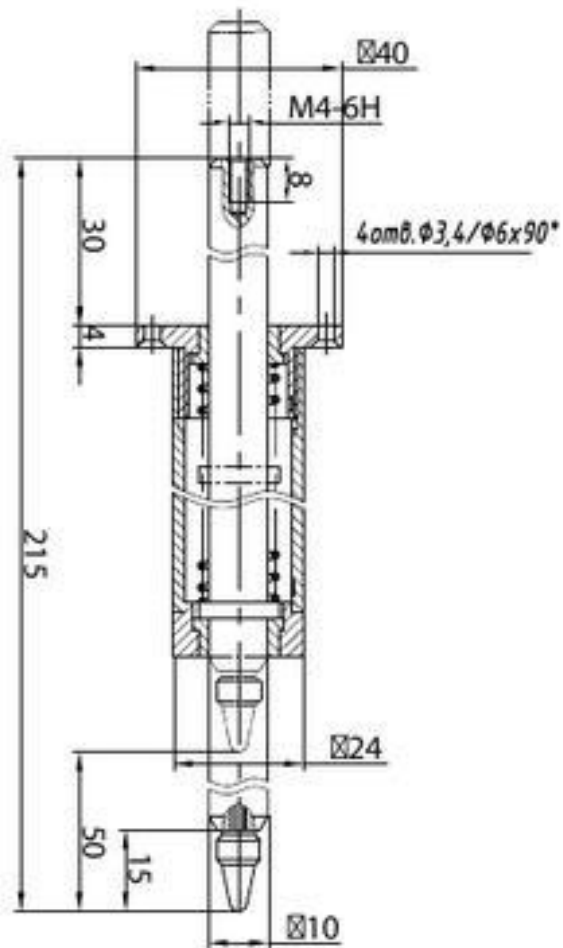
Габаритные и присоединительные размеры насадки Н(50)/С.
